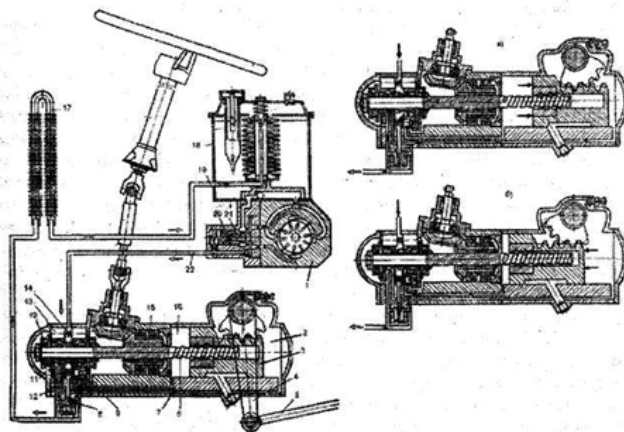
Схема работы гидроусилителя рулевого управления автомобиля КамАЗ-4310: 1-насос; 2-задняя полость; 3-поршень-рейка; 4-рулевая сошка; 5 -продольная рулевая тяга; 6-винт; 7- картер рулевого механизма; 8-обратный клапан; 9 - предохранительный клапан; 10-распределитель; 11- золотник; 12 -упорный подшипник; 13 - плунжер; 14 - пружина плунжера; 13 - угловой реактор; 16-передняя полость; 17 - радиатор; 18- бачок; 19-линия слива; 20 - предохранительный клапан
